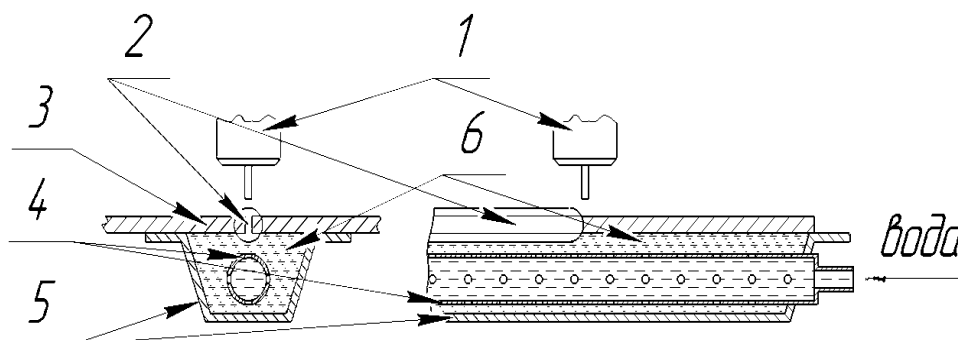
Пример теплоотвода с применением влаговпитывающих материалов: 1 – сварочная головка; 2 – сварной шов; 3 – свариваемые детали; 4 – питающая трубка; 5 – корпус охладителя; 6 – пористый или волокнистый материал
